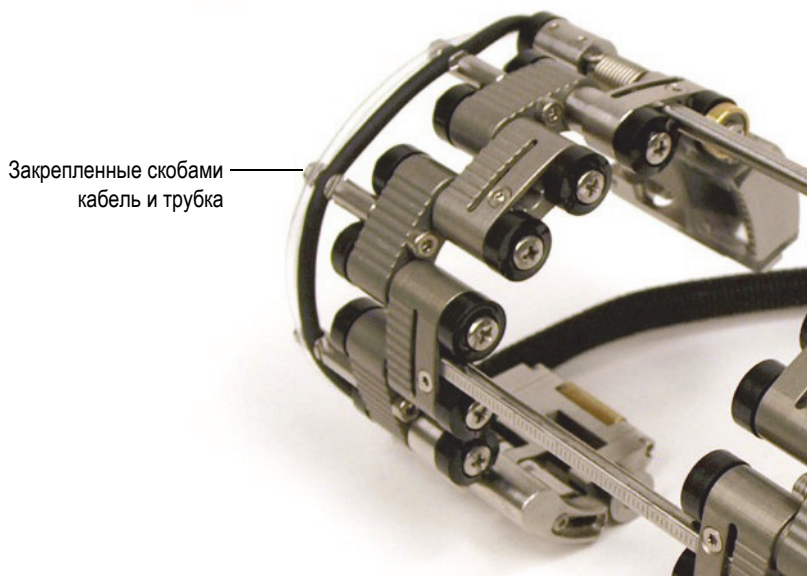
Крепление кабеля и трубки вдоль сканера
